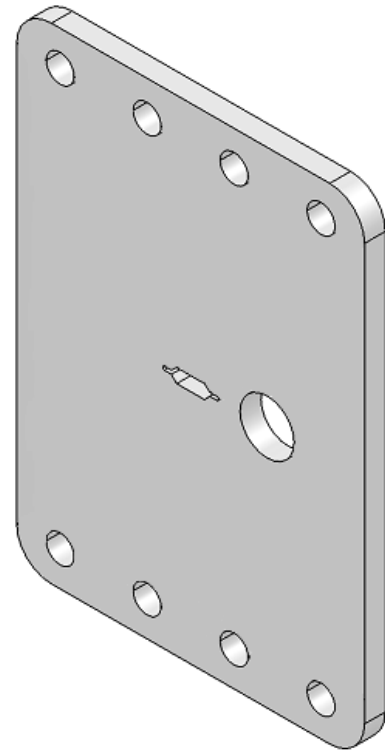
Dimensiones y Geometría de la Probeta CCT con Taladro (cotas en mm)
